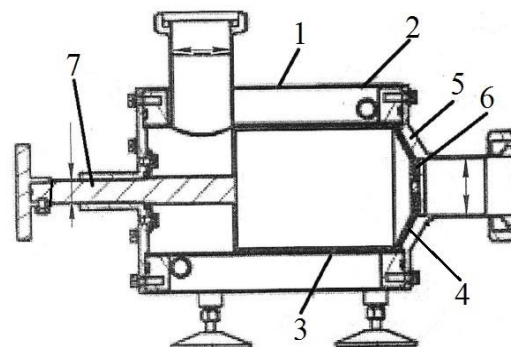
Конструкция гомогенизатора с узлом регулирования дисперсности частиц: 1 – цилиндрический корпус; 2 – теплообменная рубашка; 3 – цилиндрический поршень; 4 – направляющая опора; 5 – поверхность поршня; 6 – рабочий (формирующий) зазор; 7 – регулировочный винт
